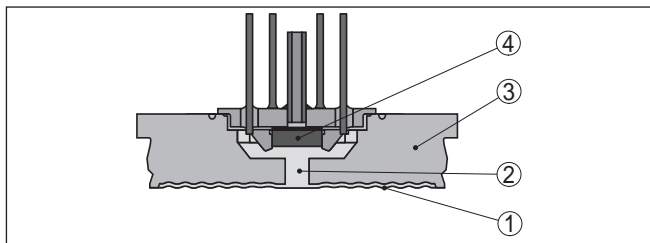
Estrutura do sistema de medição com elemento sensor piezo-resistivo
